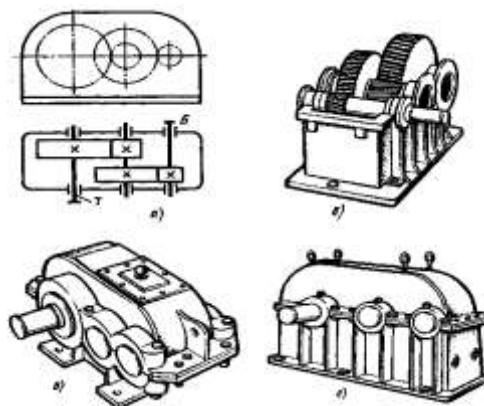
Двухступенчатый горизонтальный редуктор с цилиндрическими колесами:
